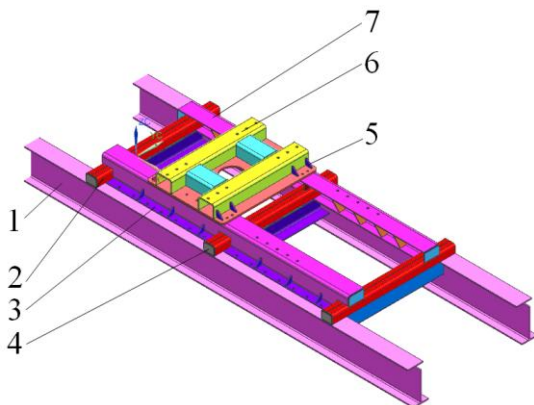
Конструкция стойки сидельно-сцепного устройства: 1 – лонжерон рамы тягача; 2 – опорная балка; 3 – пластина упорная; 4 – заглушка балки; 5 – ребро опоры; 6 – подставка седельного устройства; 7 – опорный швеллер
